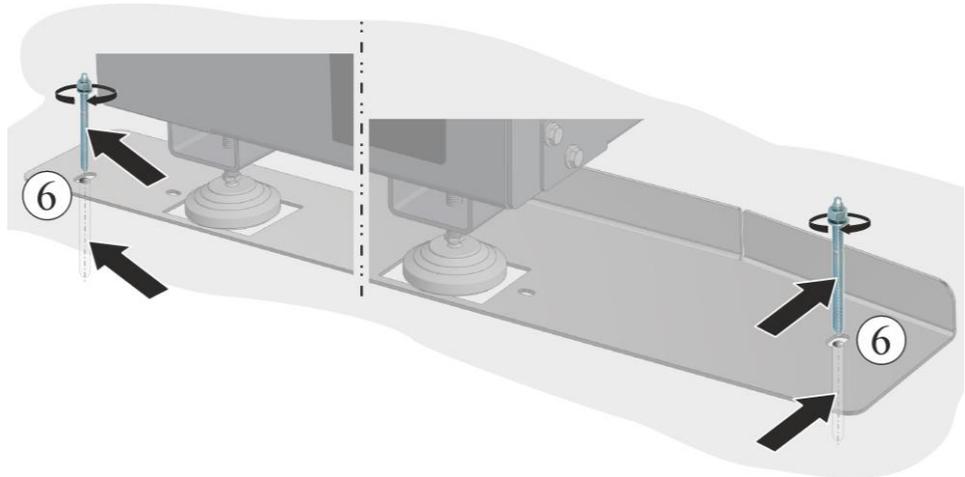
Fissare le lamiere al pavimento (illustrazione simile)
